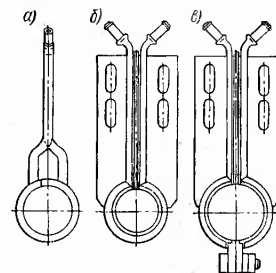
Конструкции индукторов для сварки прямошовных труб: а — многовитковый неразъемный; б — одновитковый неразъемный; в — одновитковый разъемный
